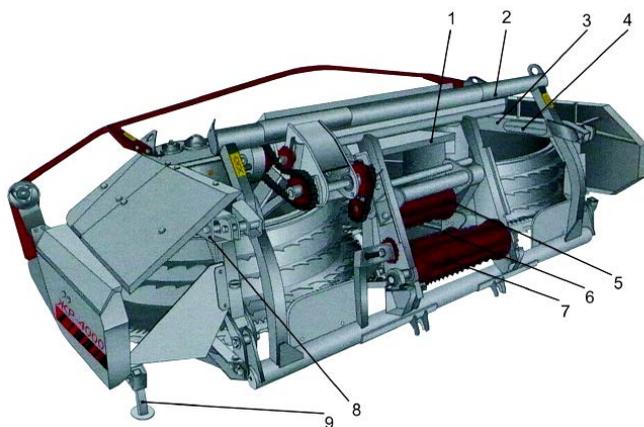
Жатка роторная ЖР-4000 (вид сзади): 1 – приемная камера; 2 – проставка; 3, 8 – балки навески; 4 – блок пружин механизма уравнивания; 5 – бiter проставки верхний; 6 – валец жатки; 7 – бiter проставки нижний; 9 – стойка жатки
